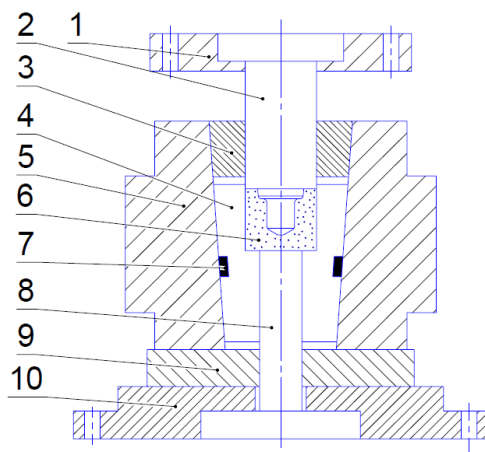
Оснастка для изготовления детали "вкладыш"
